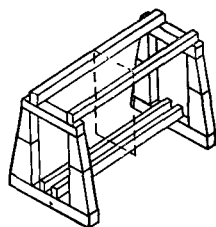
Типовые конструкции каркаса сборочного приспособления
